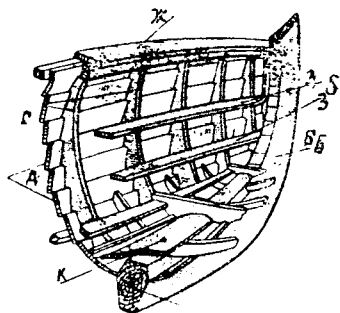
Строеніе корпуса деревянной лодки.—*Д*, обшивка.—*Ж*, привальный брусъ.—*Б*, планки рѣшетки или пола (флоръ).—Остальныя буквы объяснены на предыдущемъ рисункѣ.
